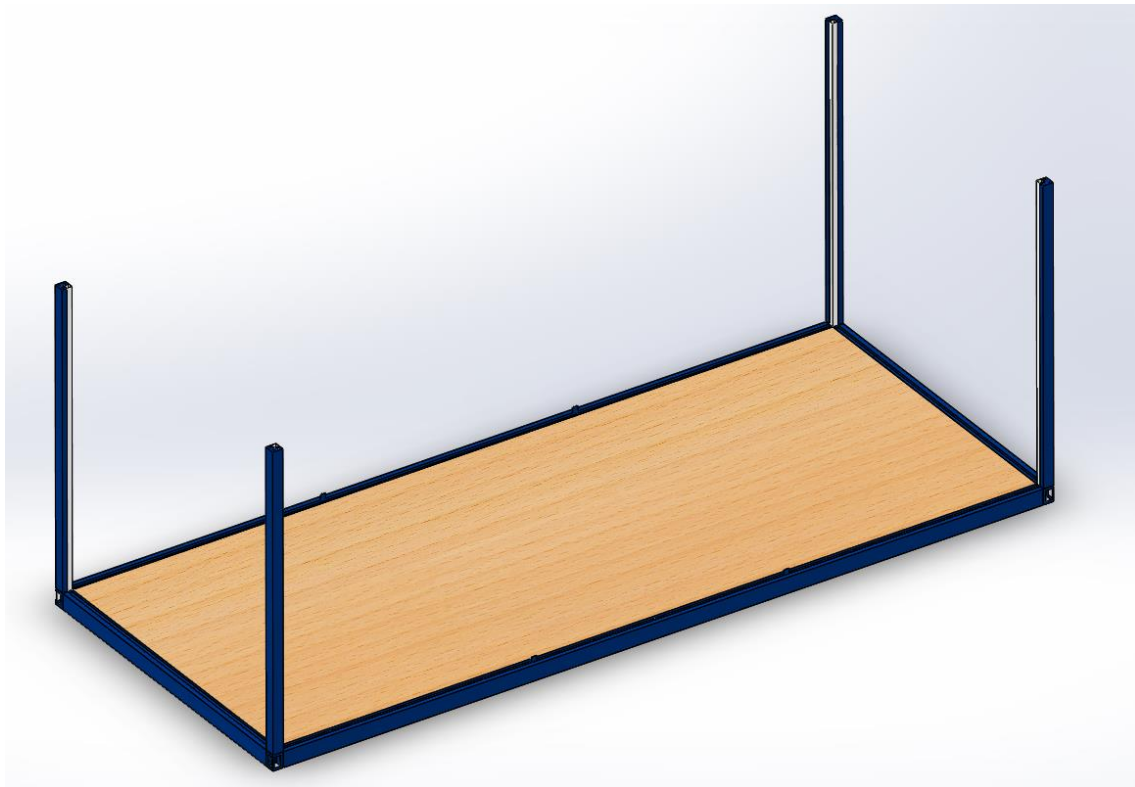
Ensamblaje Pilares y Tubos de PVC
